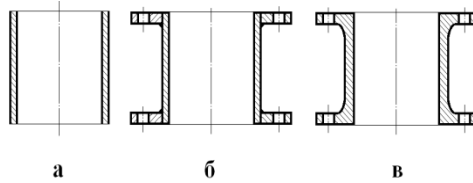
Частина корпусу ємнісного апарата:
